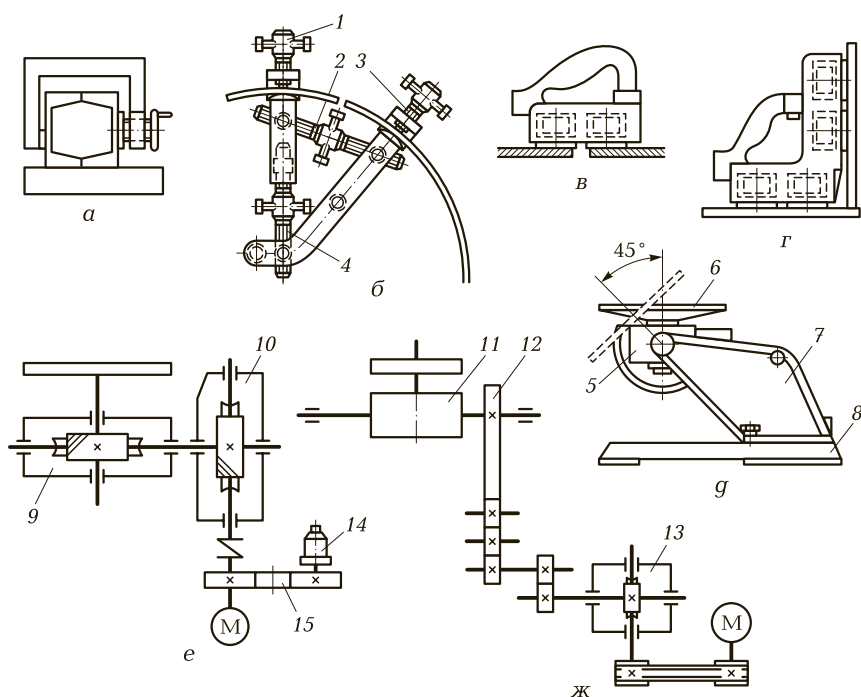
Сборочные приспособления для фиксации изделий при сварке: а — струбцина; б — винтовая стяжка; в, г — электромагнитные фиксаторы соответственно для фиксации зазора и сборки стыковых и угловых соединений; д — манипулятор; е, ж — кинематические схемы механизмов вращения и наклона манипулятора; 1, 3 — винтовые струбины; 2, 4 — винты; 5, 11 — поворотные столы; 6 — планшайба; 7 — корпус; 8 — опора; 9, 10, 13 — червячные редукторы; 12 — зубчатый сектор; 14 — тахогенератор; 15 — зубчатое колесо; М — электрический двигатель
